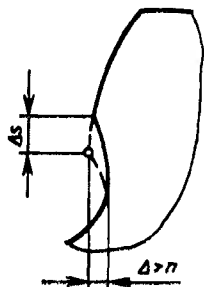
Схема срезания активного участка эвольвентного профиля зубьев заготовки фрезой с протуберанцем
